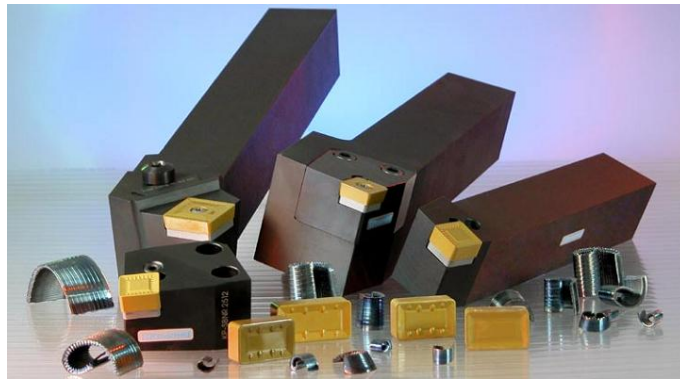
Різальні інструменти (Pramet), що рекомендовані для обточування деталей на важких верстатах
